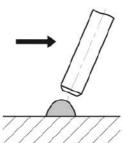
Влияние длины дуги и скорости сварки.
